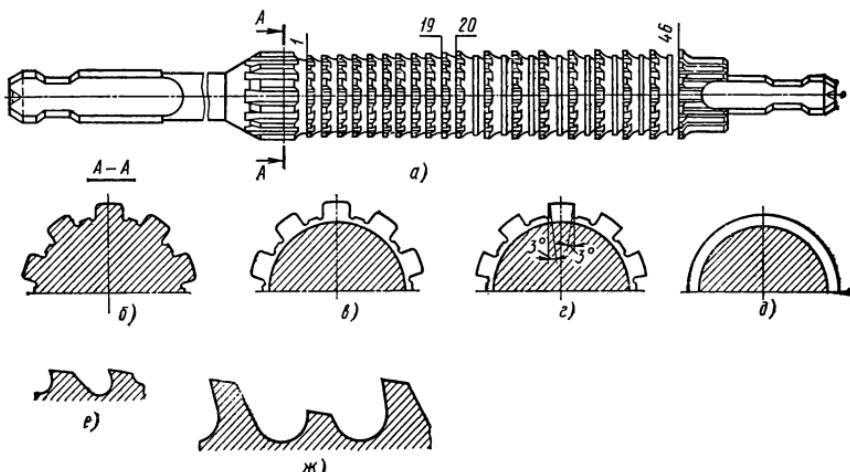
Шлицевая калибрующая протяжка с переменной схемой резания:
